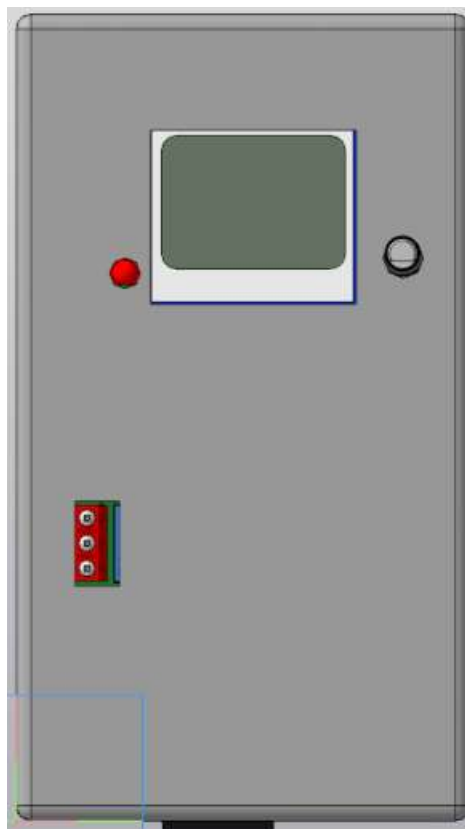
3D модель пристрою в корпусі, вид зверху
